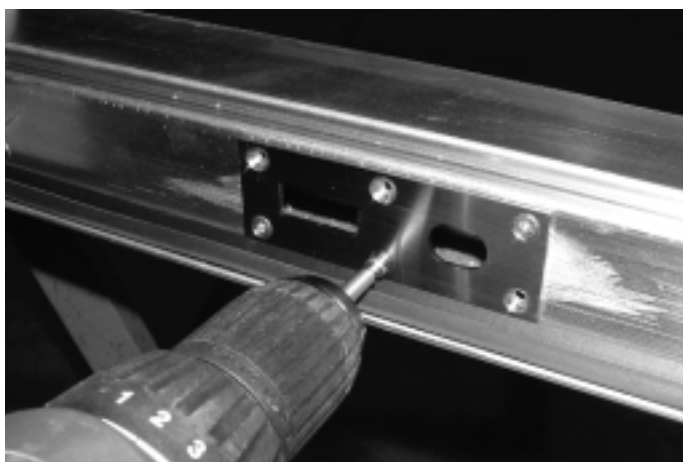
Befestigung Schliessbleche mit Senkschraube M4x12 (557.046)
